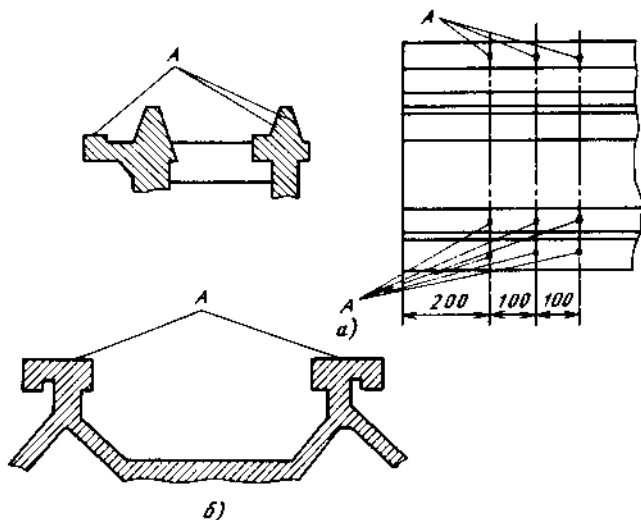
Схема нанесения лунок на направляющих токарно-винторезных (а) и фрезерных (б) станков: А — места нанесения лунок
